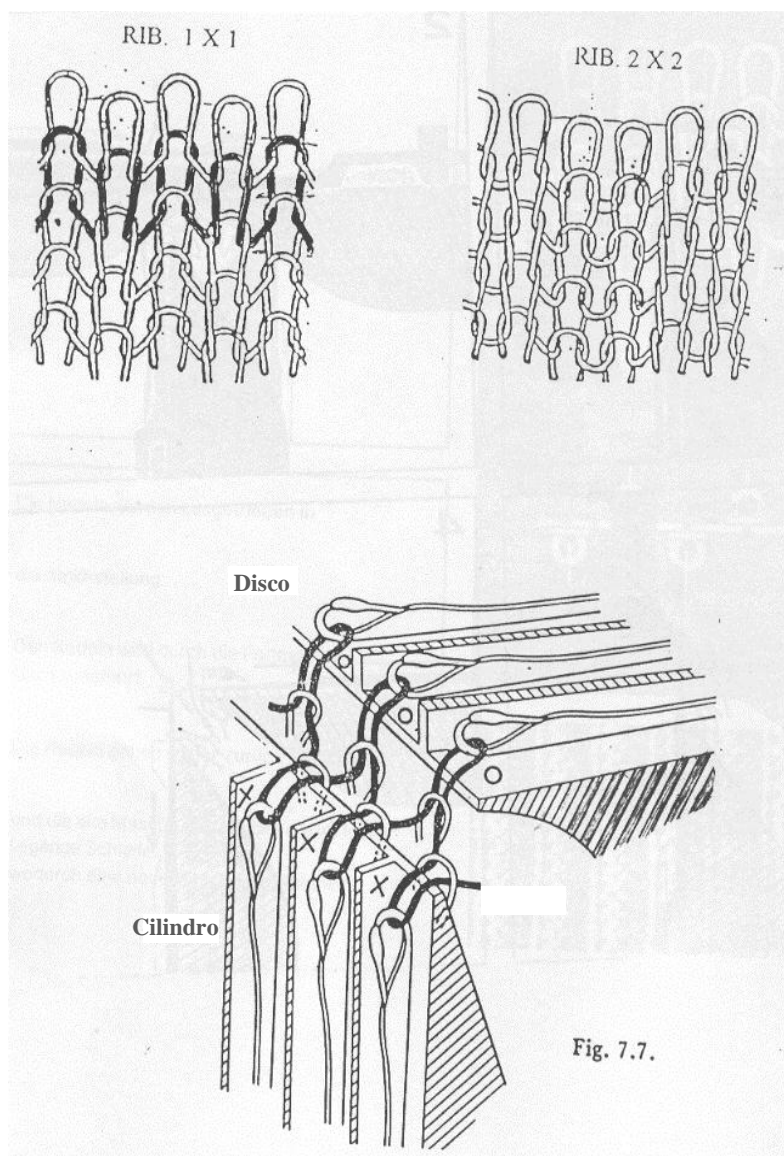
Estruturas de Malhas em Rib e Disposição das Agulhas
